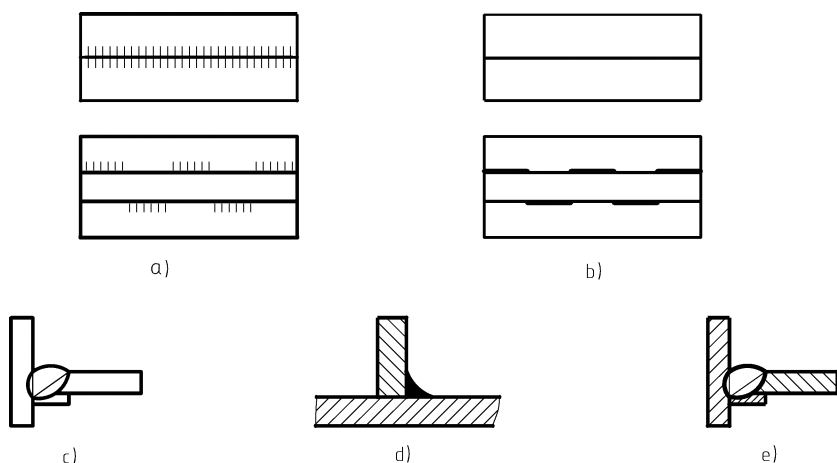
焊缝的视图及剖视（断面）图画法
